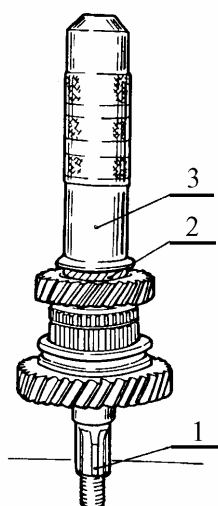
Напрессовка втулки шестерни на ведущий вал:
